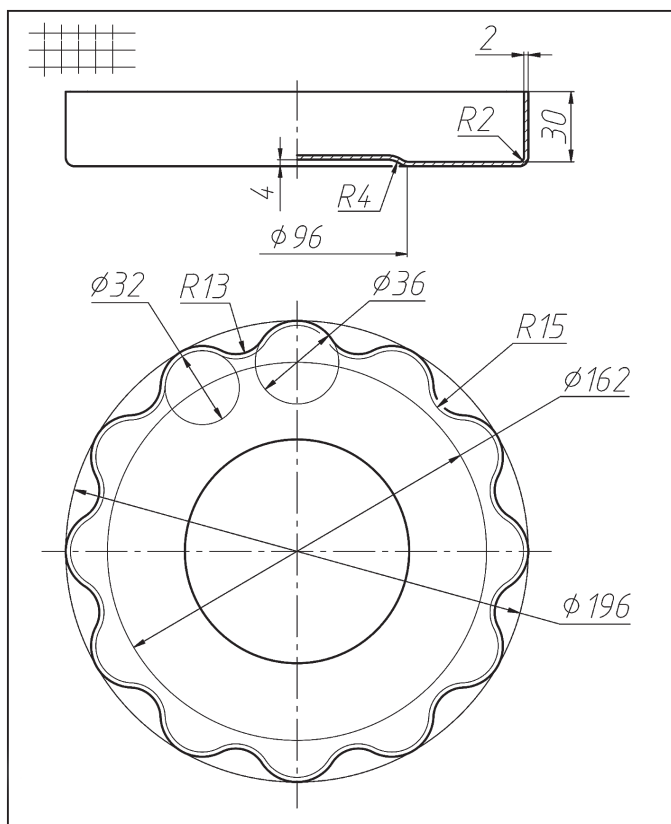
Эскиз детали «Форма пищевая прямая» с натурного образца
